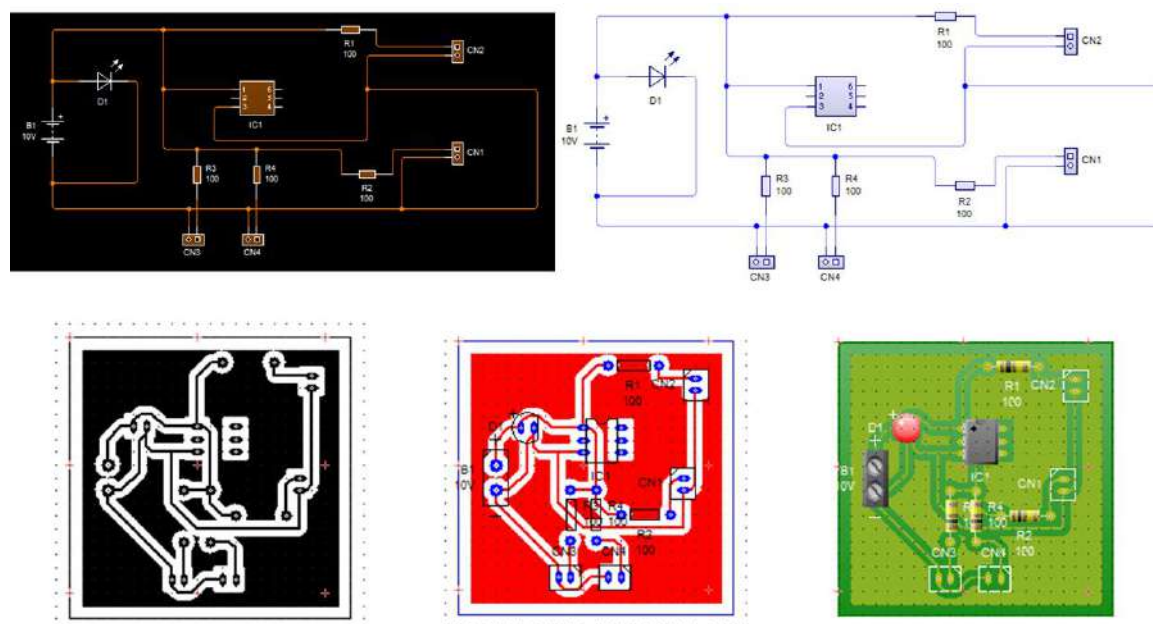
Diseño de la placa secundaria construido con LiveWire y PCB Wizard Tenelema, 2022
